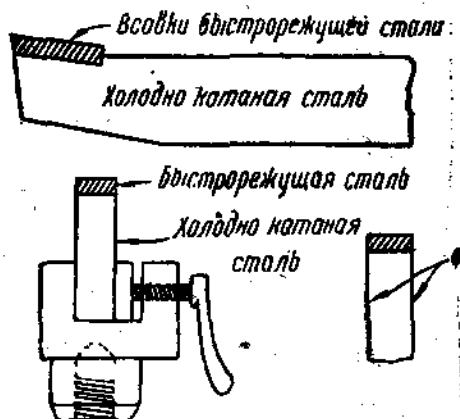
Зажимное приспособление при очень тонкой пластинке быстрорежущей стали.
